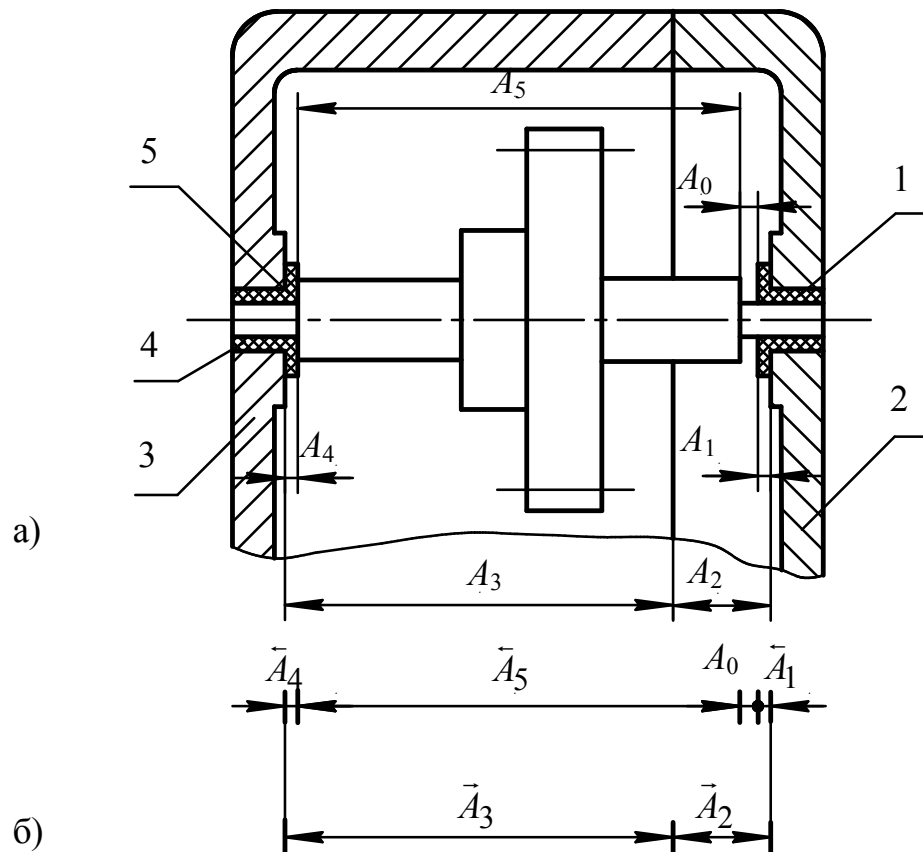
Схематичне креслення редуктора й розмірний ланцюг
